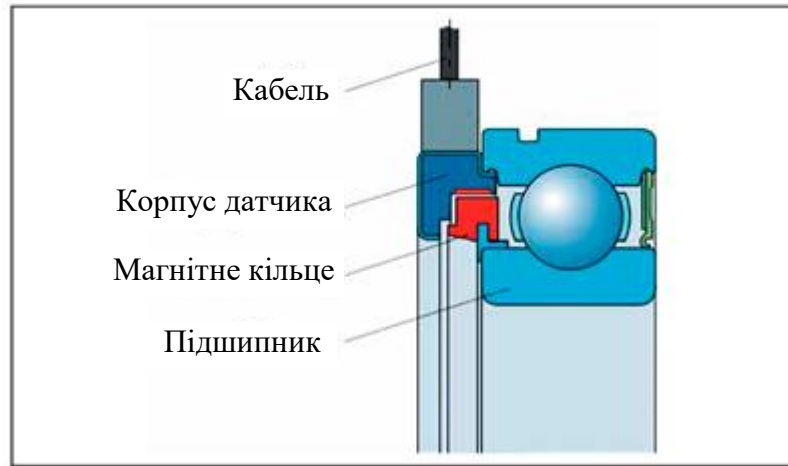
Вигляд підшипника з датчиками обертання
